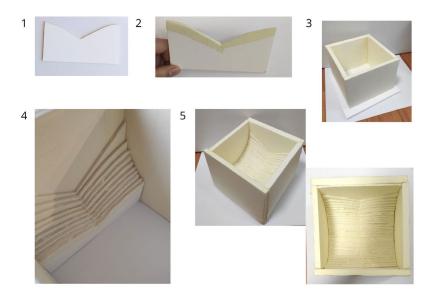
Desarrollo del molde. Fuente: Fuente: Serena Jiménez Maki, GDA1C (2023)
